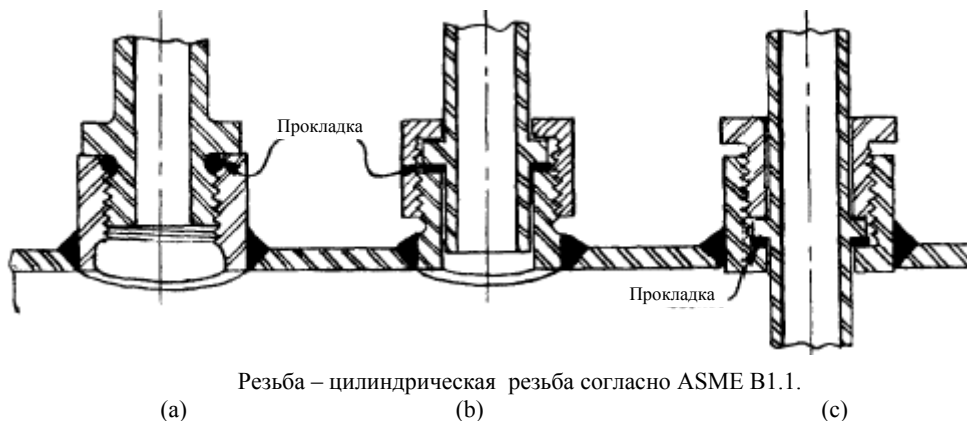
Типовые резьбовые соединения, использующие цилиндрическую резьбу.
